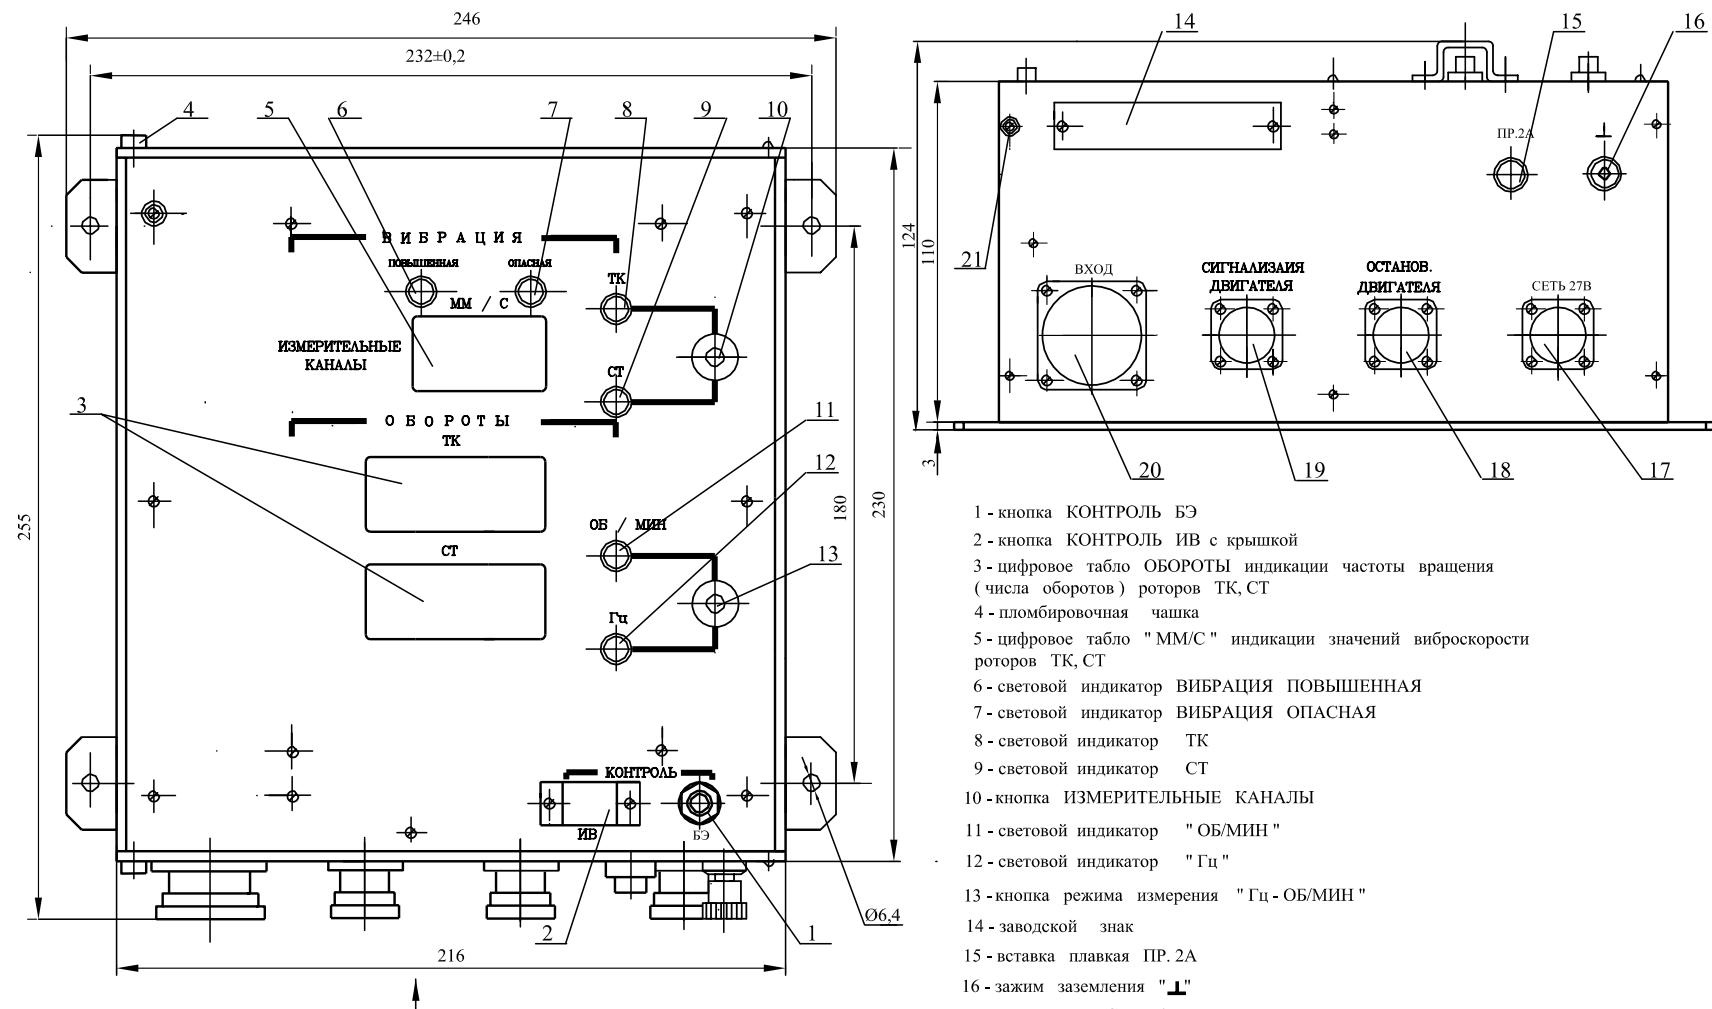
Габаритно-установочные размеры блока БЭ-39-1М.3.2-01
